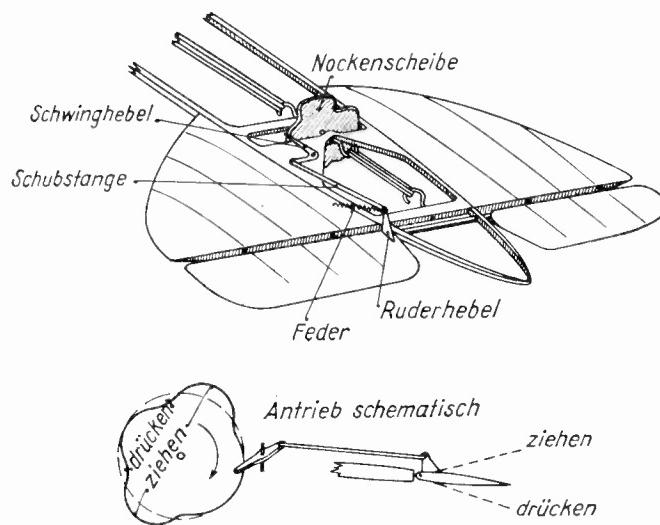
Steuerungsautomat von Gummimotor angetrieben.
